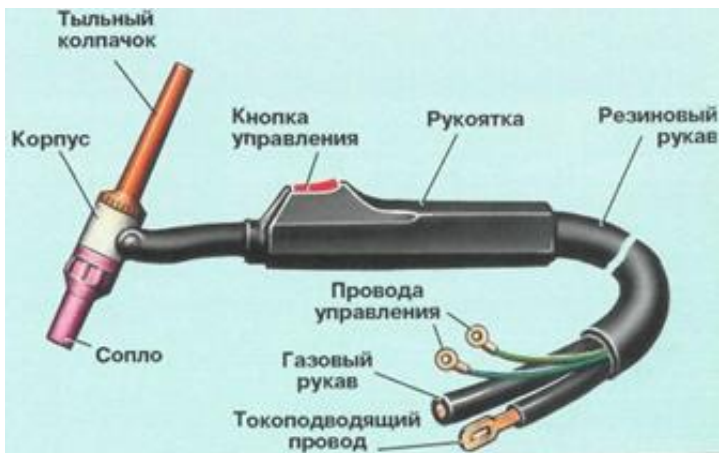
Горелка для сварки неплавящимся электродом
